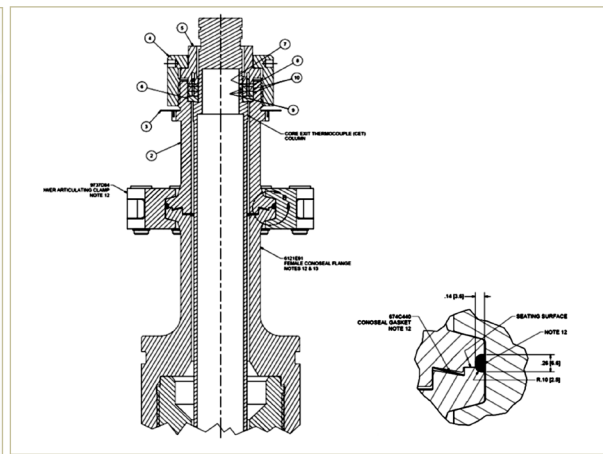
Configuración final - conjunto de cierre CETNA con la soldadura de sellado.
